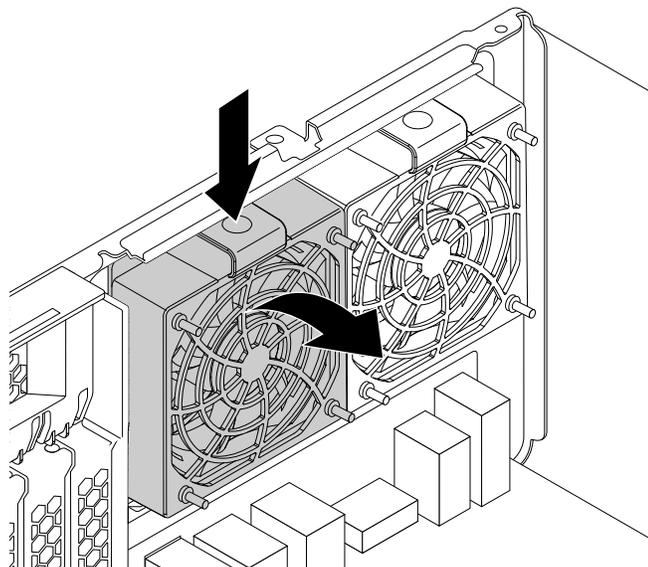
Lüftungsbaugruppe an der Rückseite entfernen
